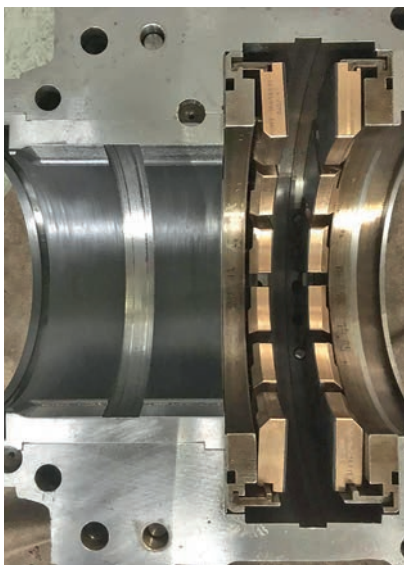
Опорно-упорный подшипник ротора турбины низкого давления после 3016 ч эксплуатации
